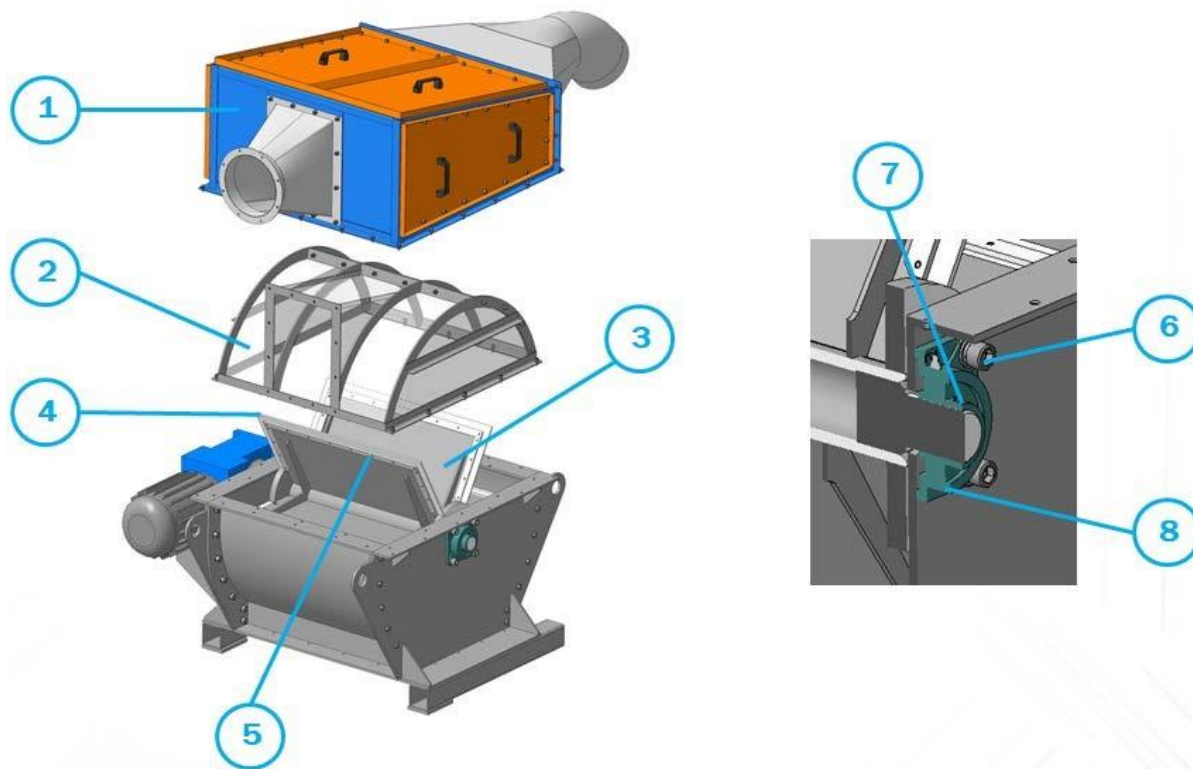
Схема замены уплотнителей и корпусного подшипника затвора.
